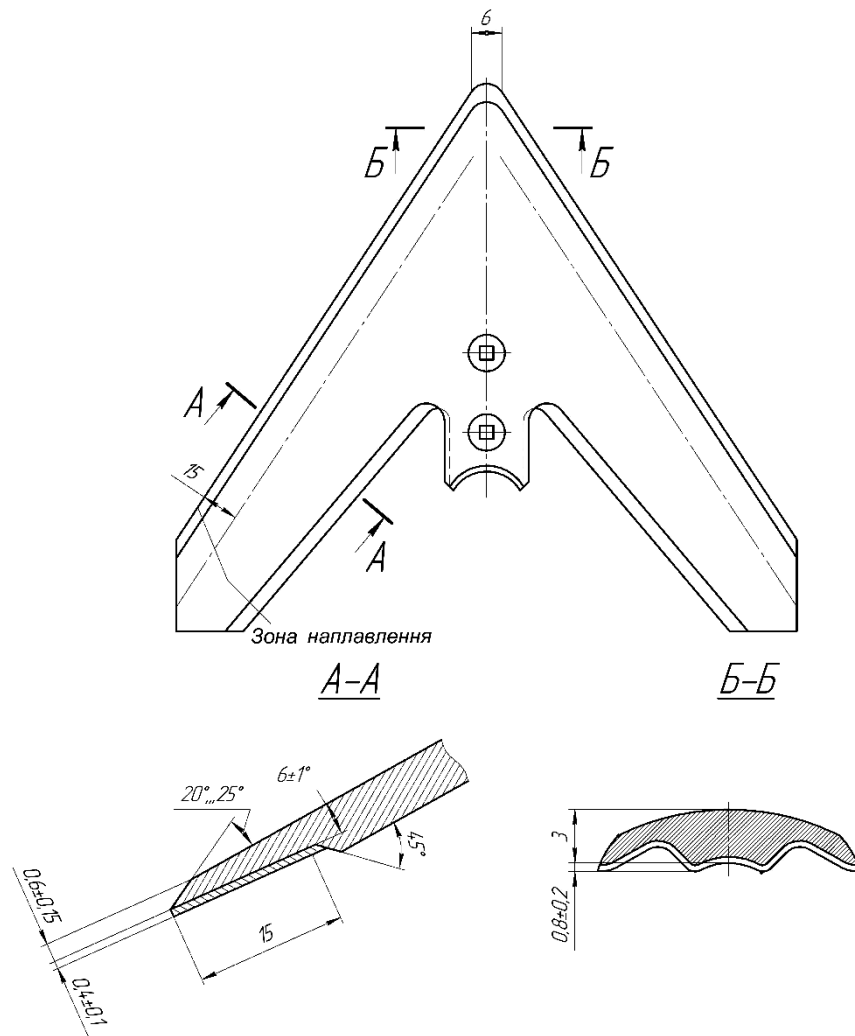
Лапа, що самозагострюється конструкції ГОСНИТИ, з нижньою наплавкою [2]
